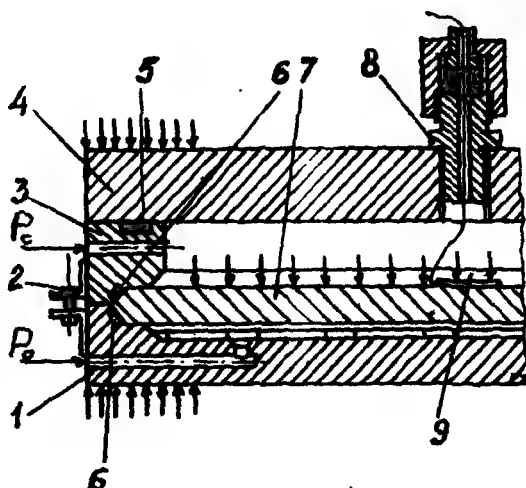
Камера для испытаний элементов сварных конструкций при повышенном давлении агрессивной среды
